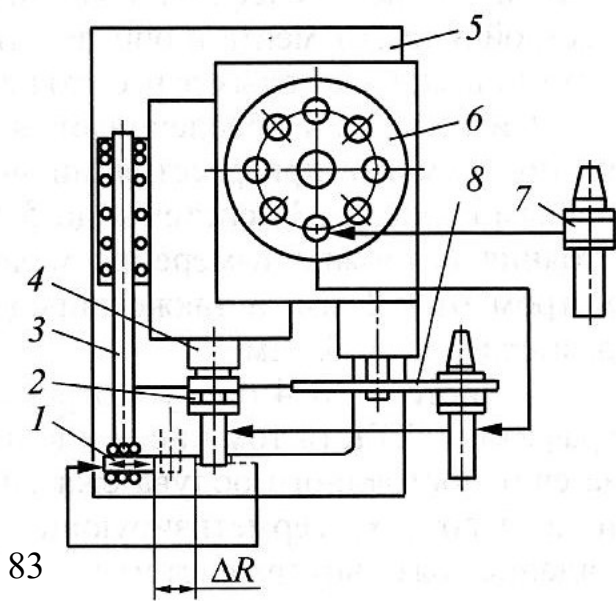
Схема размерной настройки расточного инструмента на станке
